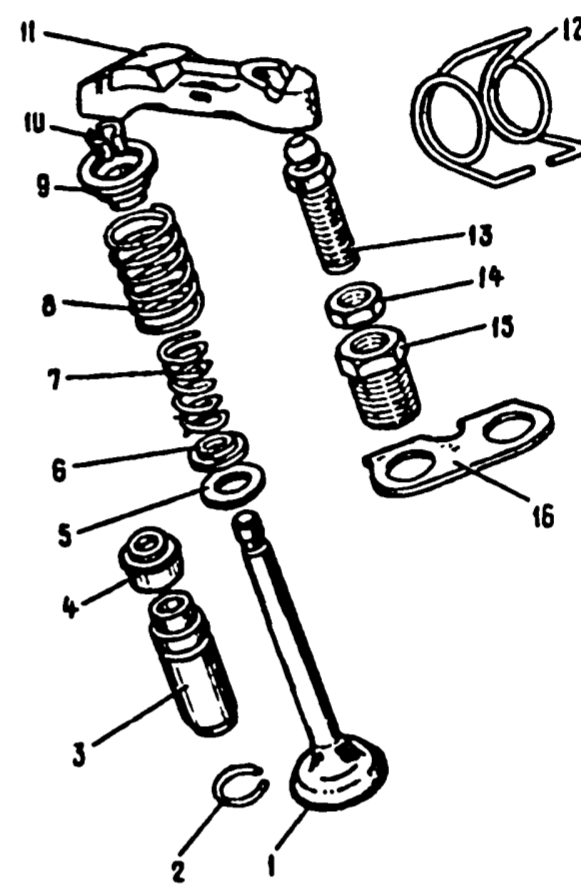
Детали клапанного механизма: 1 - клапан; 2 - стопорное кольцо; 3 - направляющая втулка; 4 - маслоотражательный колпачок; 5 - опорная шайба наружной пружины; 6 - опорная шайба внутренней пружины; 7 - внутренняя пружина; 8 - наружная пружина; 9 - тарелка пружины; 10 - сухари; 11 - рычаг привода клапана; 12 - пружина рычага; 13 - регулировочный болт; 14 - контргайка регулировочного болта; 15 - втулка регулировочного болта; 16 - стопорная пластина пружины рычага
